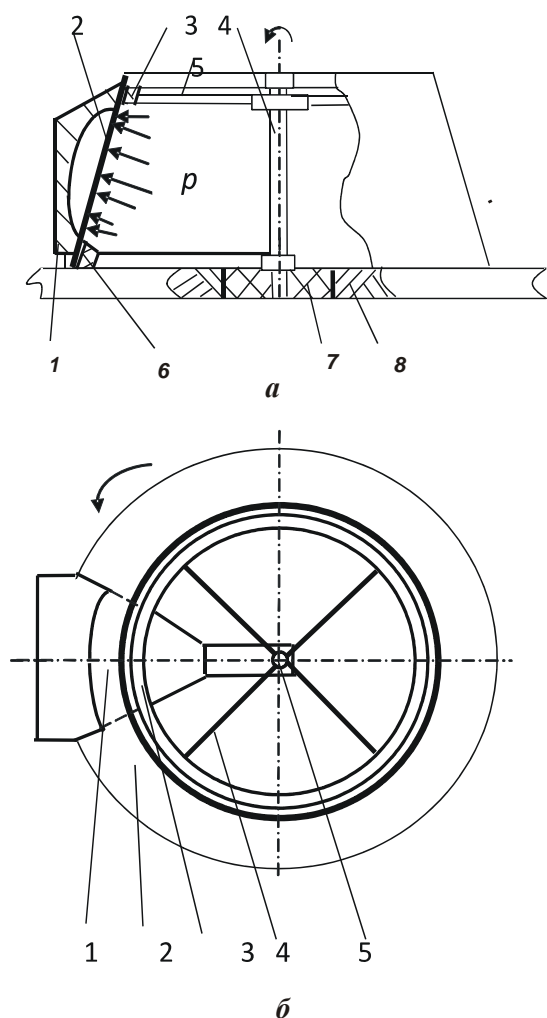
Схема стандовой штамповки с использованием термофизических методов локальной штамповки: фронтальный (а) и горизонтальный (б) вид: 1 – матрица-сектор; 2 – пространственный полуфабрикат; 3 – прижим; 4 – упор; 5 – ось; 6 – основание; 7 – втулка
